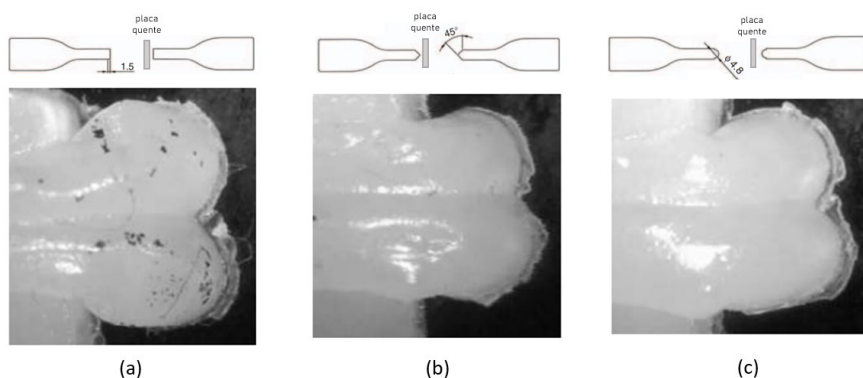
Micrografia PP soldado a placa quente a 260°C, com deslocamento de soldagem de 0,4 mm, por 60 s: exemplo do efeito de contato insuficiente na superfície da solda
